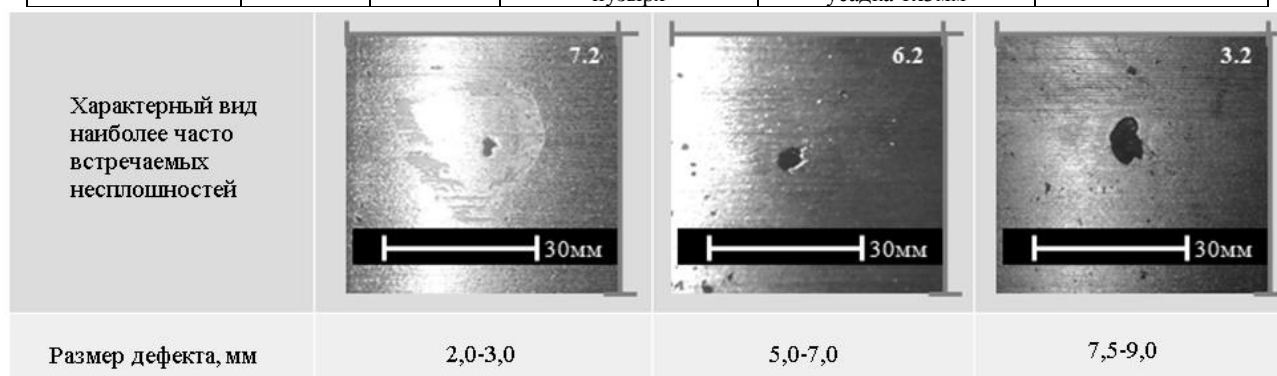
Вид типичных визуально наблюдаемых дефектов на торце кратной непрерывнолитой сортовой заготовке из стали 60С2: порезка на пилах
